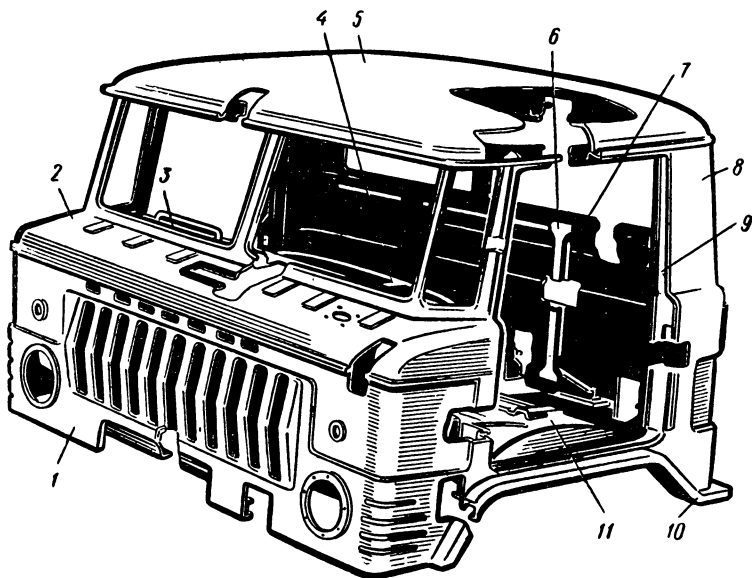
Корпус кабины автомобиля ГАЗ-66:
